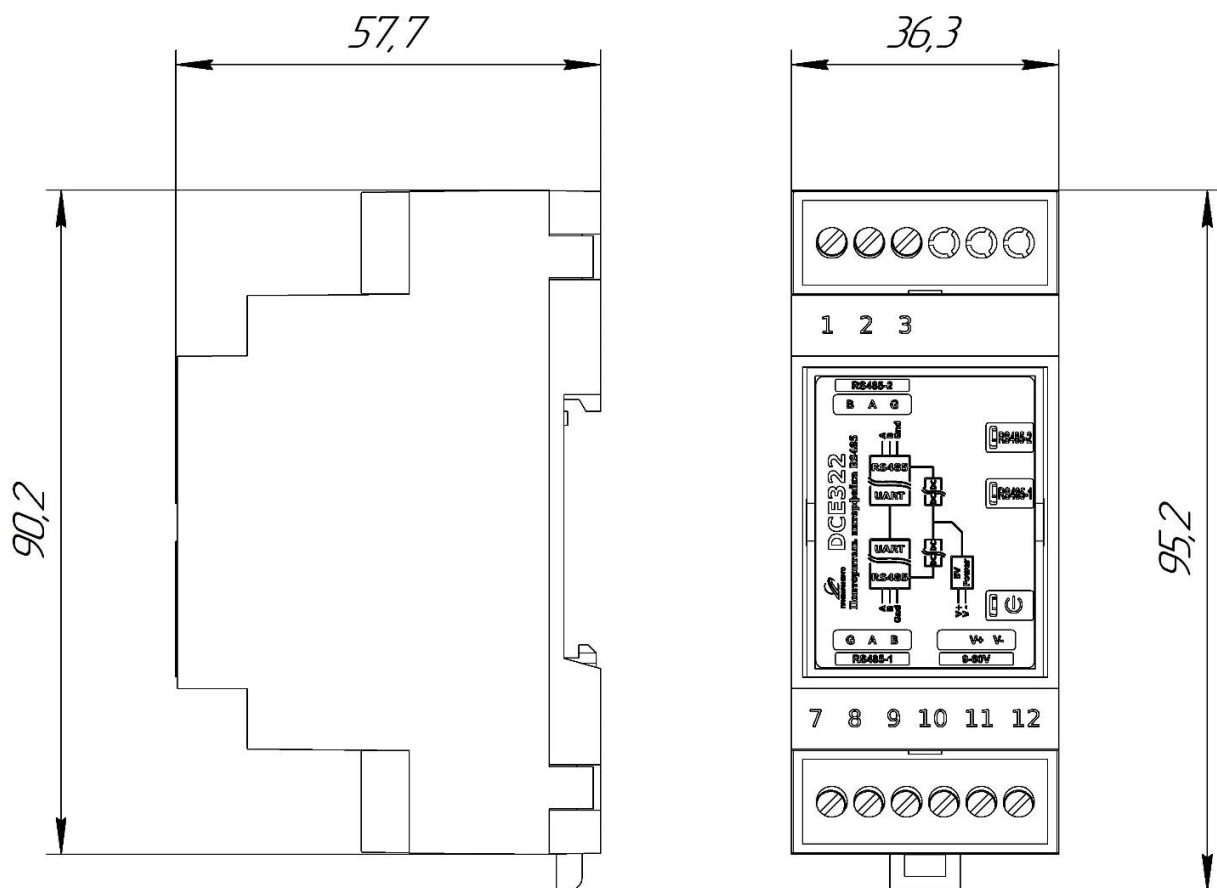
Габаритные размеры повторителя интерфейса RS-485 DCE322
